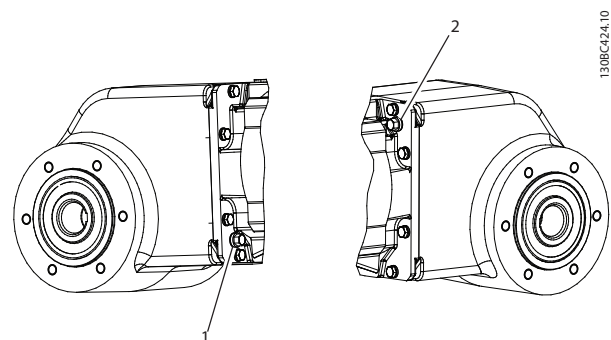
OneGearDrive Ölschrauben 1 und 2
